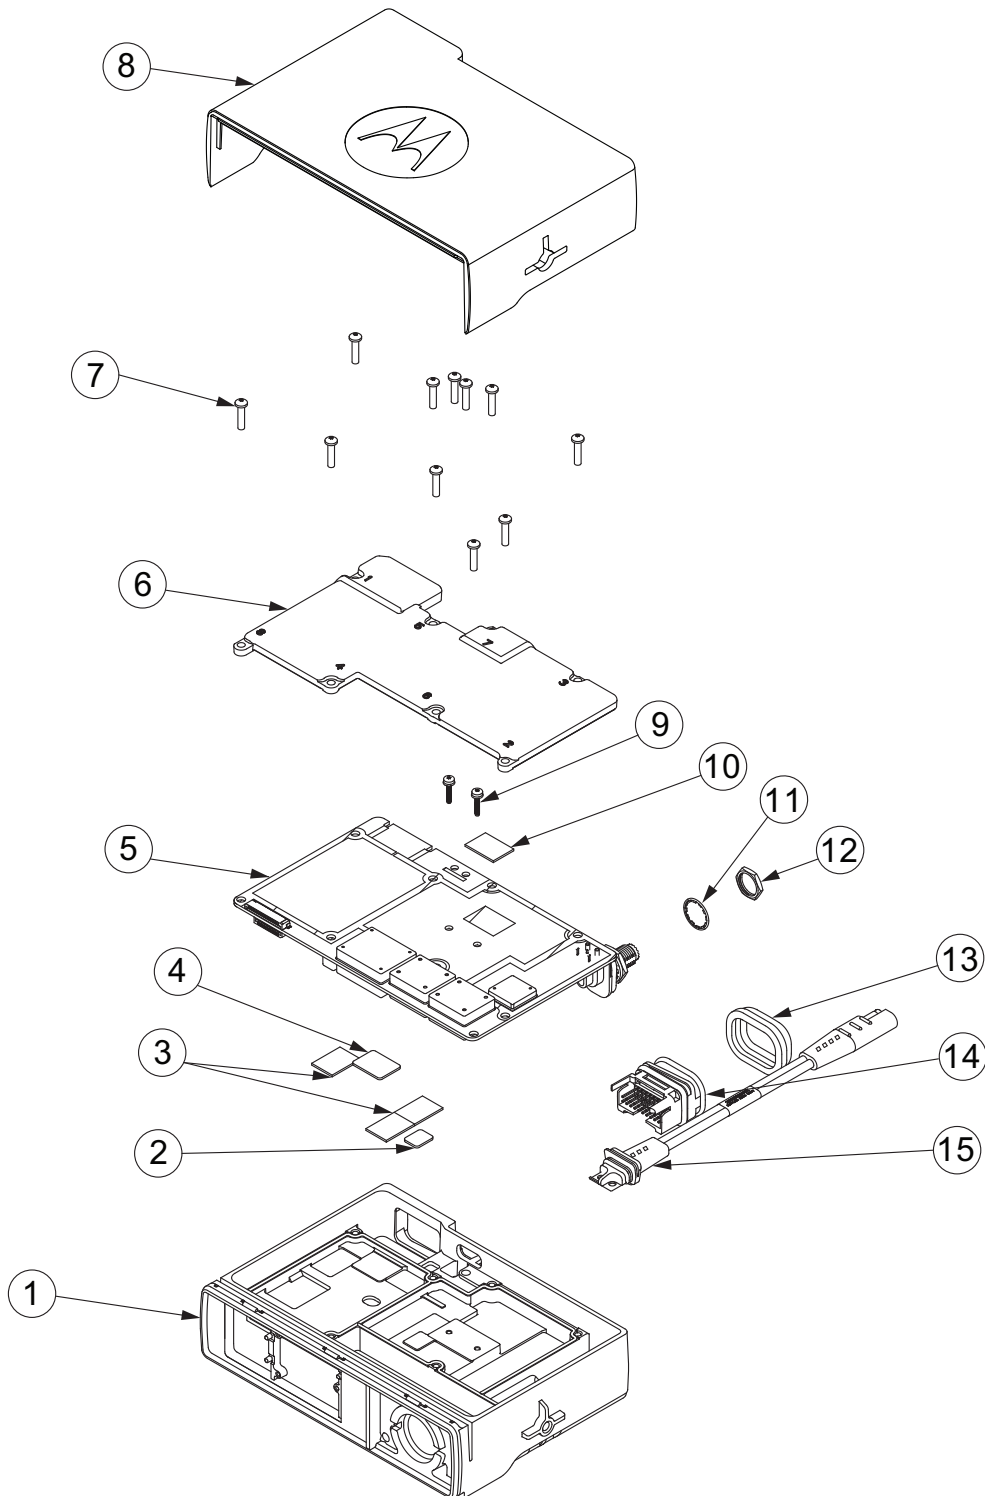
Explosionsansicht Funkgerät-Baugruppe
